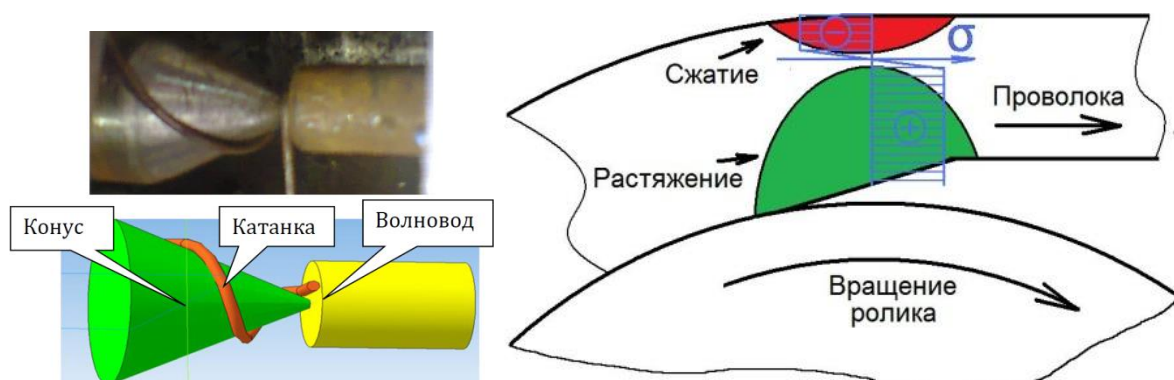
Схема и фотография траектории движения катанки (проволоки) в инструменте, а также схема области схода катанки с ролика
